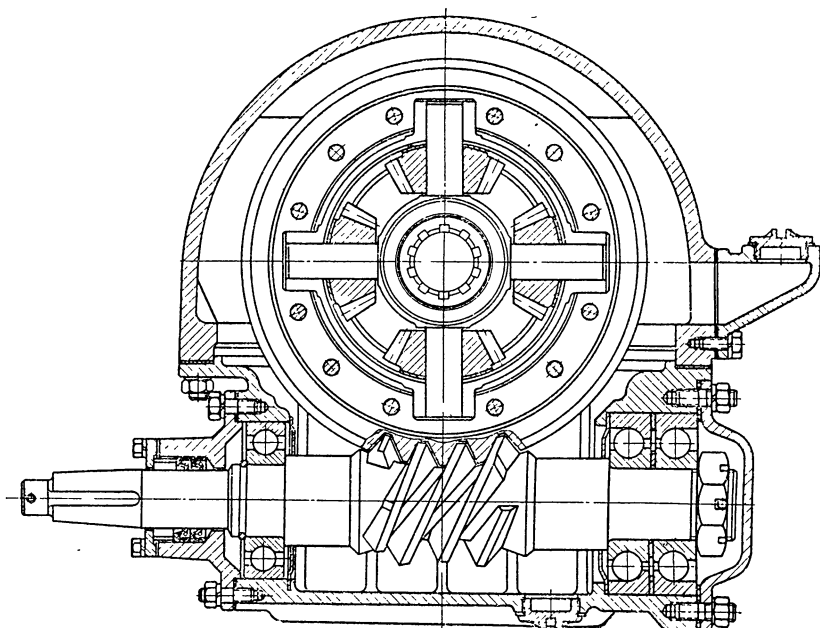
Привод транспортера породопогрузочной машины ППМ-4 с трехступенчатым редуктором и с глобоидным редуктором.
